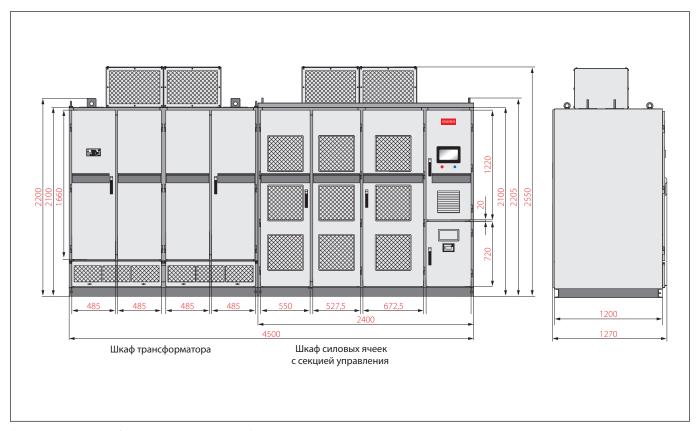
Корпус SA03 на напряжение 6 кВ
